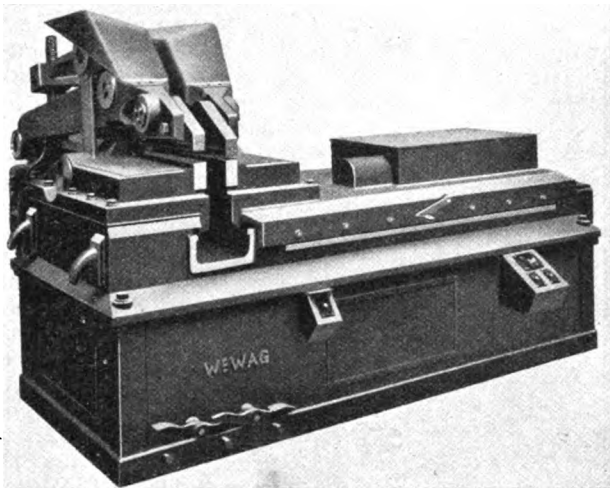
Stumpfschweißmaschine für Großoberflächenquerschnitte.
